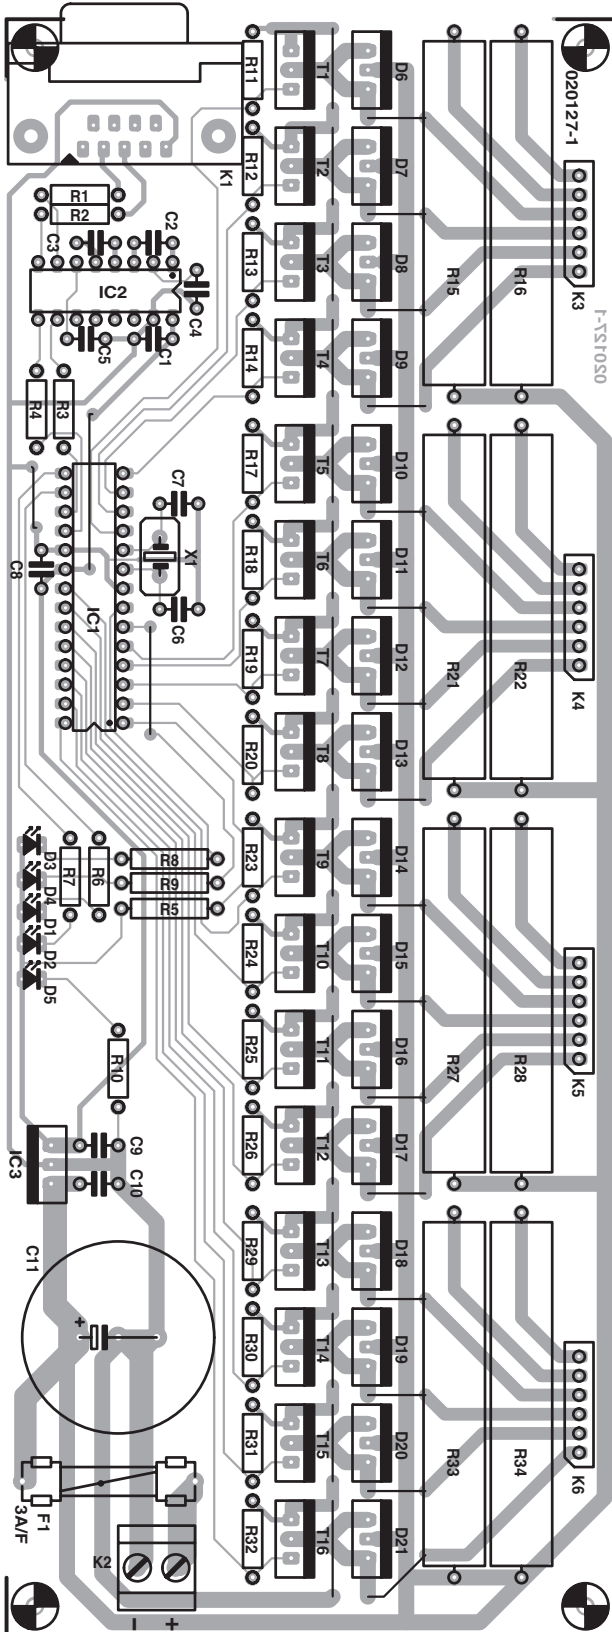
Diseño de la PCB para la placa del controlador del motor paso a paso.
